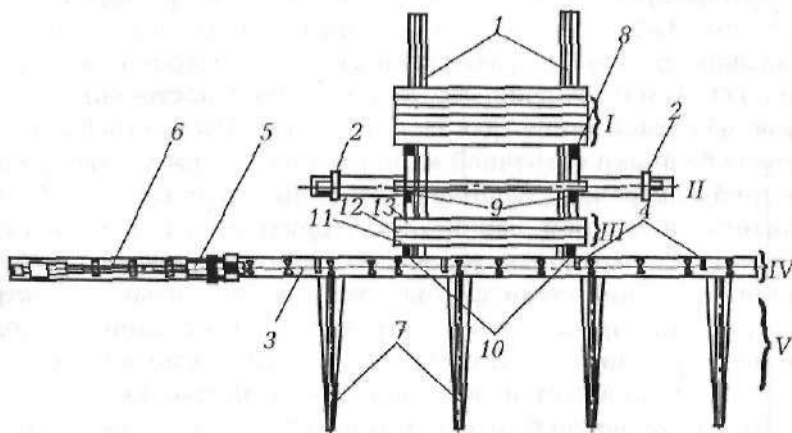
Механизированная трубосварочная база для контактной стыковой сварки оплавлением:
